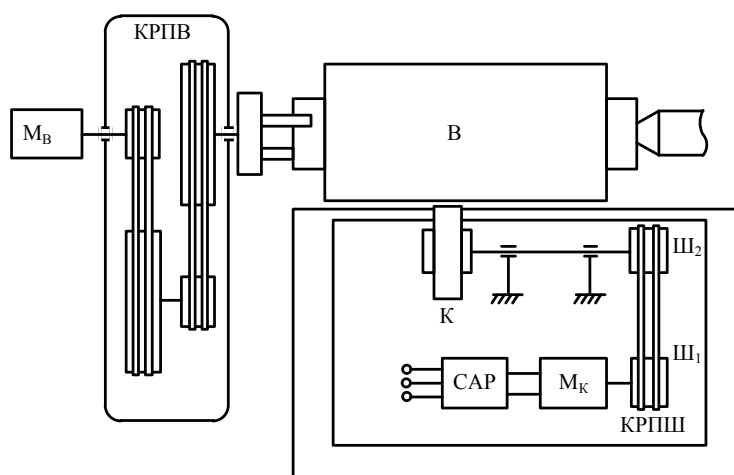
Кинематическая схема вальцешлифовального станка
